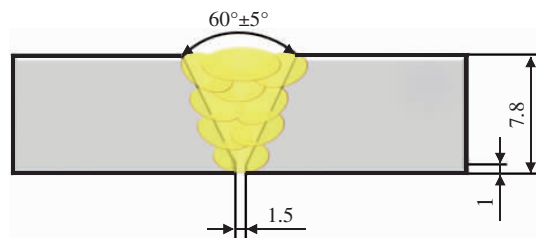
TIG 过程焊道排布及坡口尺寸形貌图
